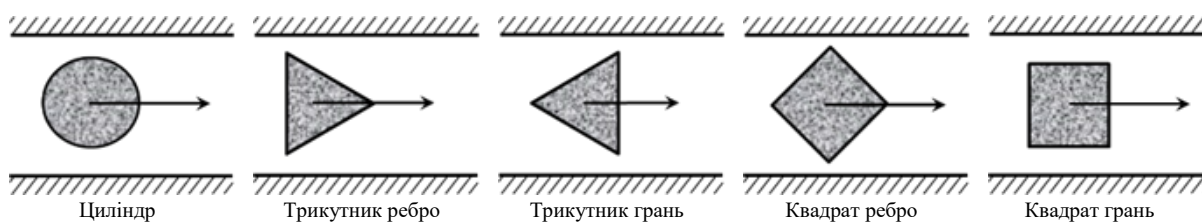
Форми деталей та особливості їх розташування під час оброблення
